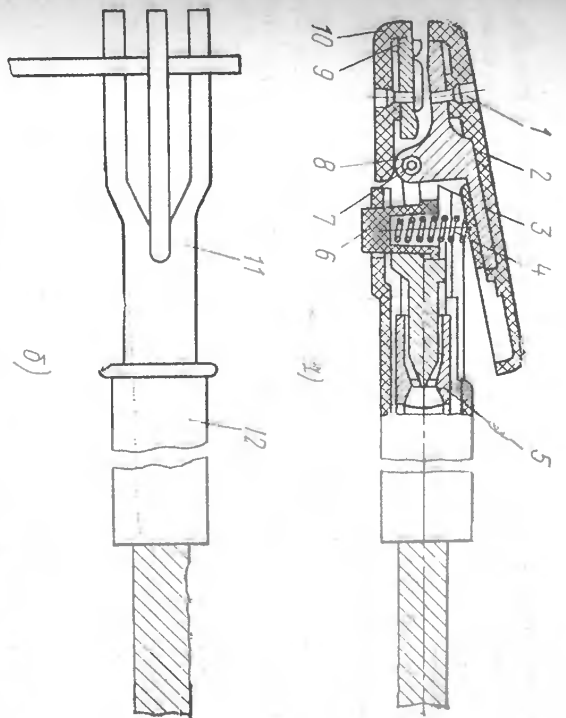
Электроподдержатели для ручной дуговой сварки: а — пассатижный (ЭД-3104У), б — вилочный: 1 — винт, 2 — 10 — верхняя и нижняя накладки, 3 — рычаг, 4, 9 — пружины, 5 — гайка, 6, 8 — втулки, 7 — ось, 11 — токопровод, 12 — рукоятка
